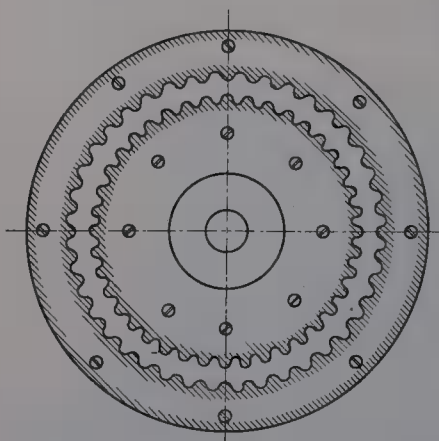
Polringe der Frankeschen Maschine (S. & H.).
